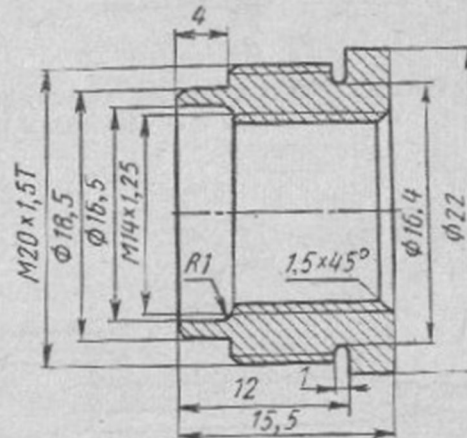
Чертеж втулки ремонтной под свечное отверстие
